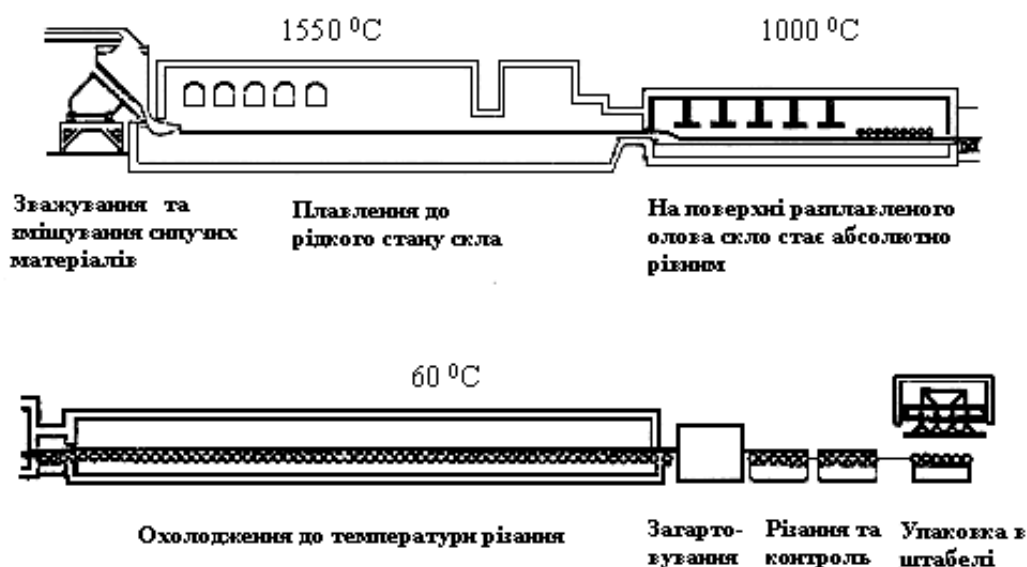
Схема процесу виготовлення флоат-скла.
